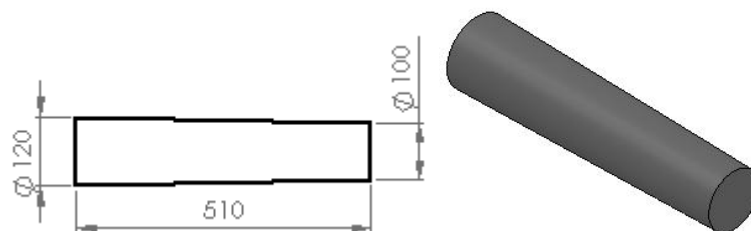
Dimensões e vista isométrica do mandril (em milímetros).
